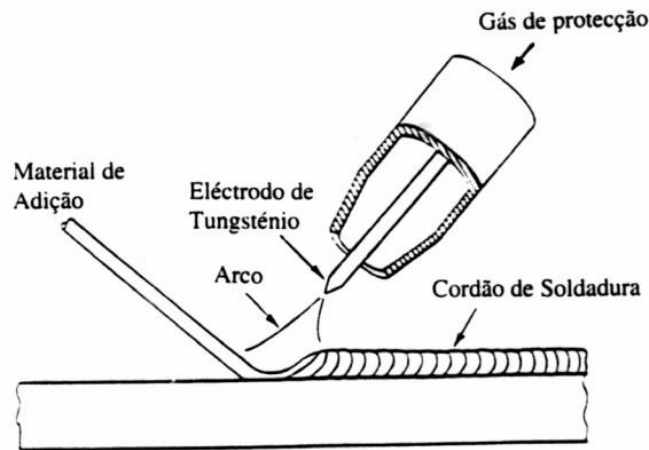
Representação esquemática do processo de soldadura TIG (fonte: utl).
